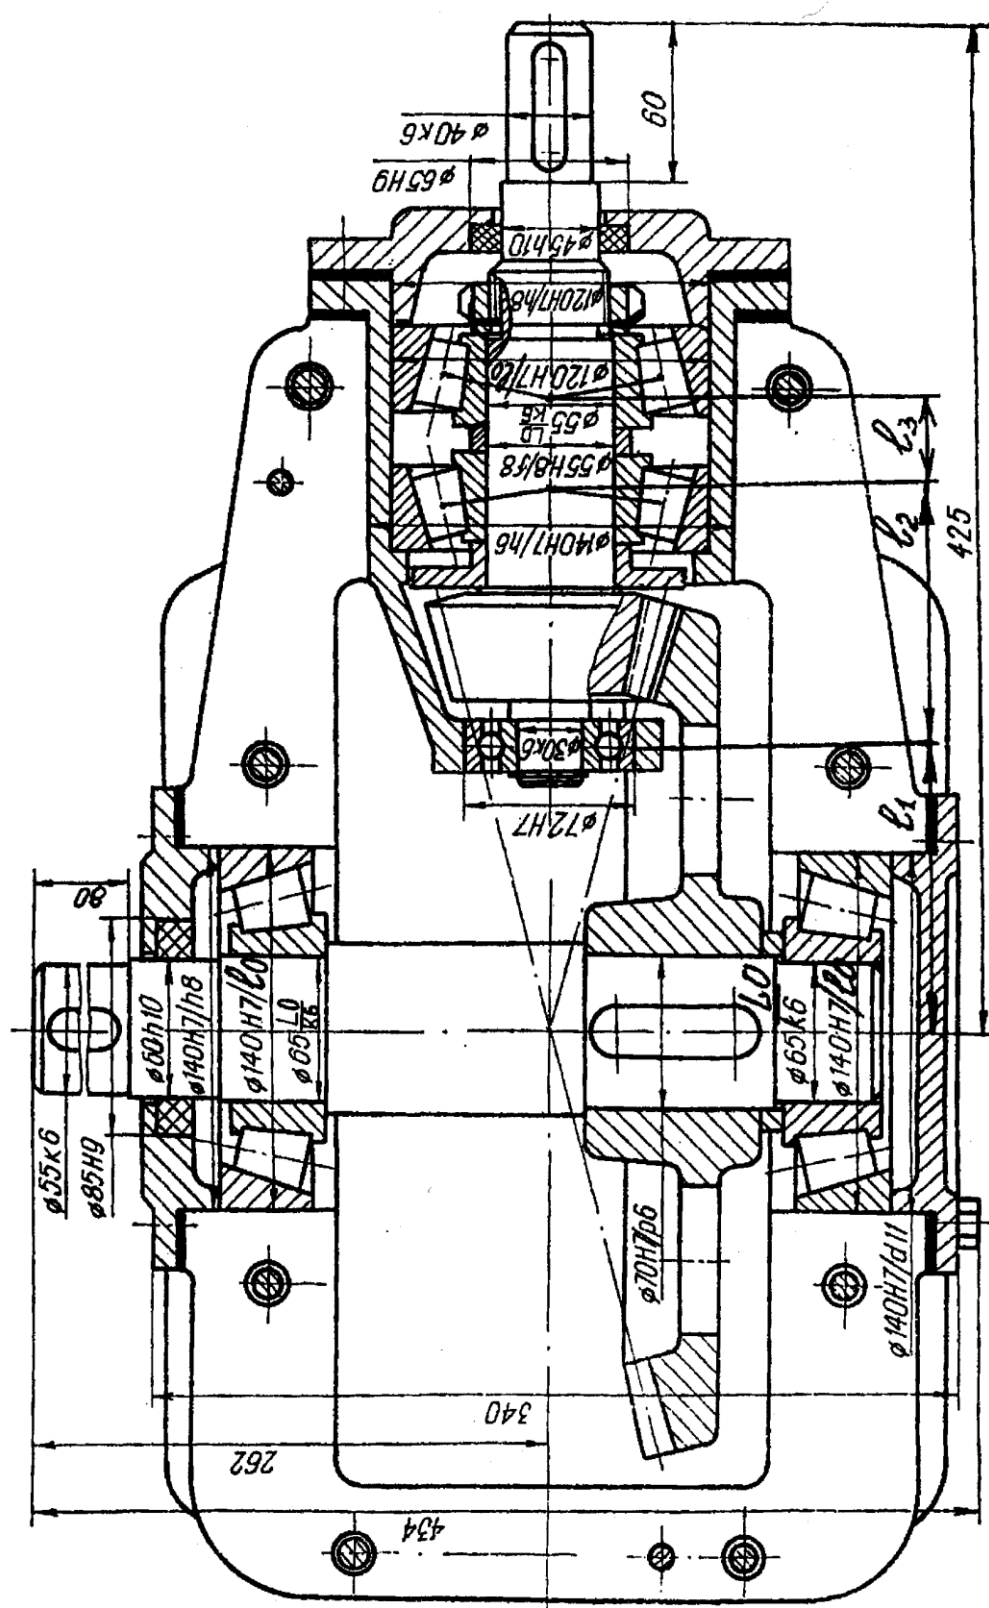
Одноступенчатый конический редуктор (шестерня установлена между опорами)
